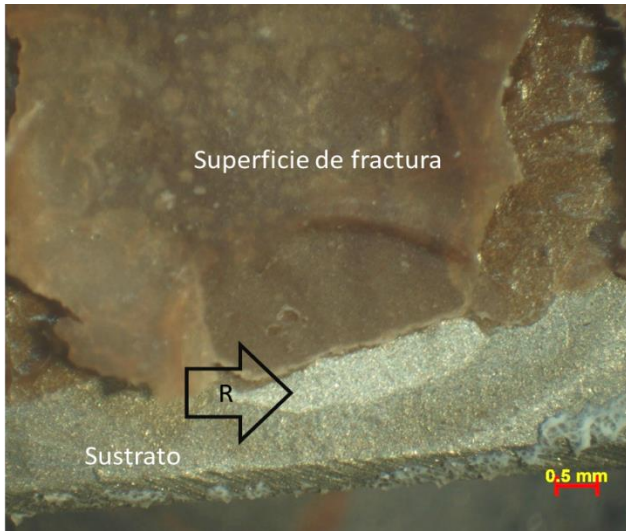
Superficie de fractura de probeta de tensión de unión aluminio-acero (7X de magnificación). Fuente: elaboración propia
